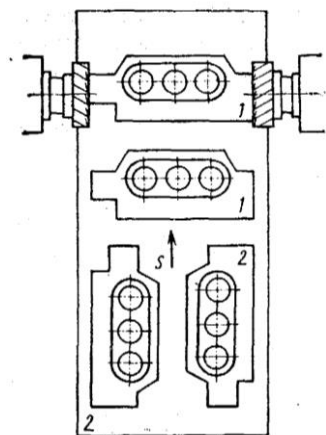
Фрезерування заготовок корпусних деталей в перекладку
